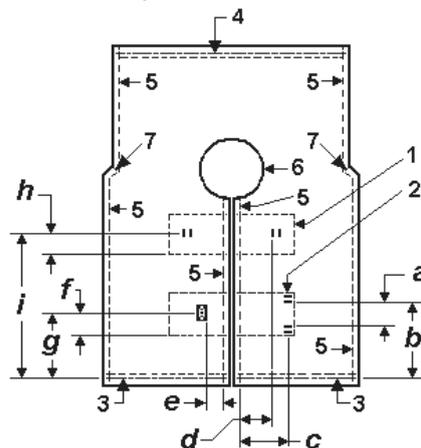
Conjunto de tira pectoral (parte ajustable izquierda y parte fija derecha)
